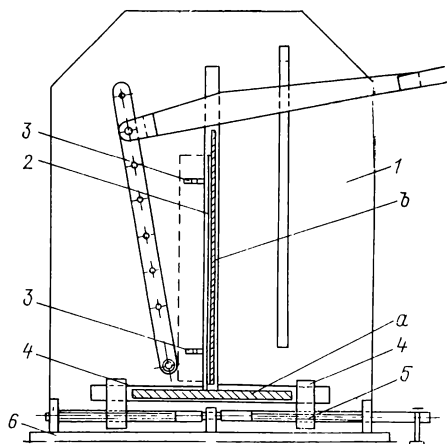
Неповоротный кондуктор для сборки тавровых балок.
